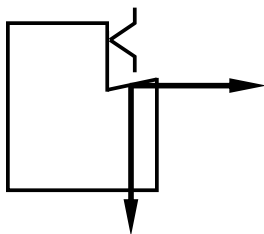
Схема крепления специальной твердосплавной пластины
